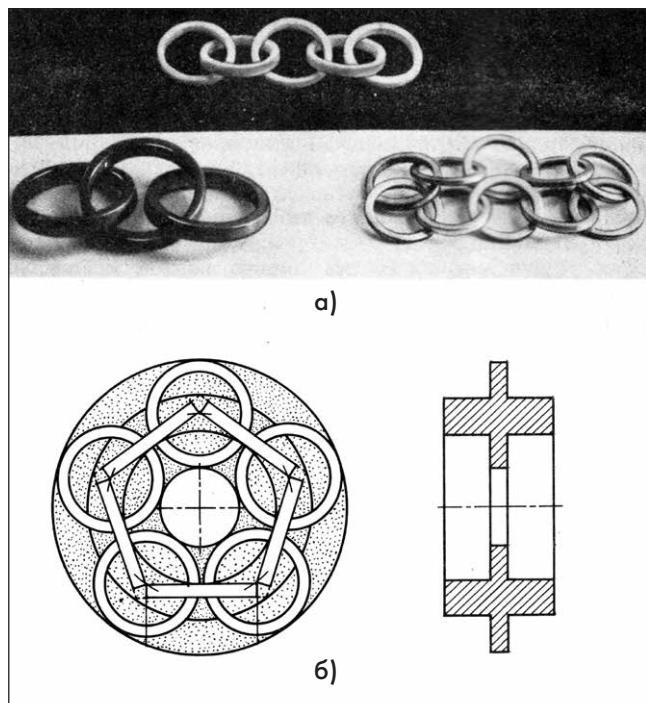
Цепи: а) из фторопластика, бронзы и дюралюминия, б) эскиз заготовки на 10 колец
